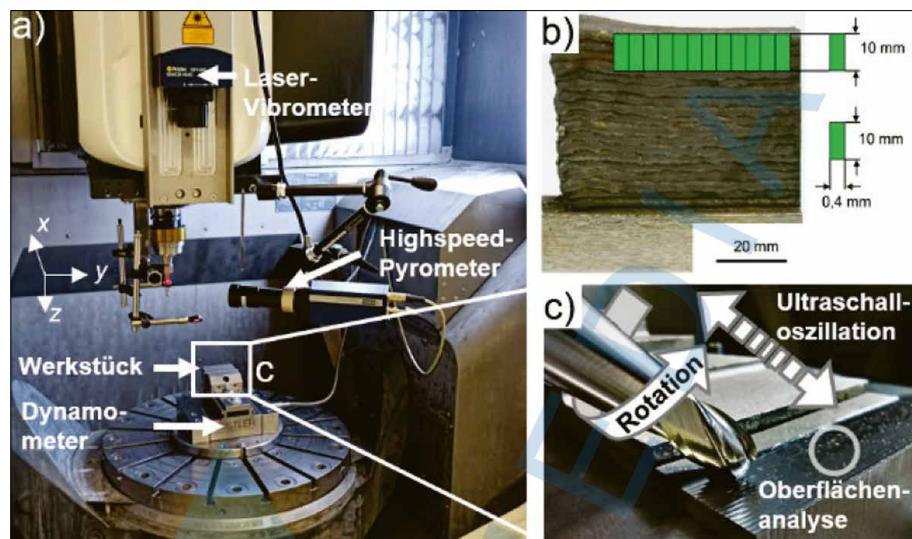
Aufbau Fräsversuche (a), Probenentnahme/-geometrie (b) und Detail Werkzeugeingriff (c).
